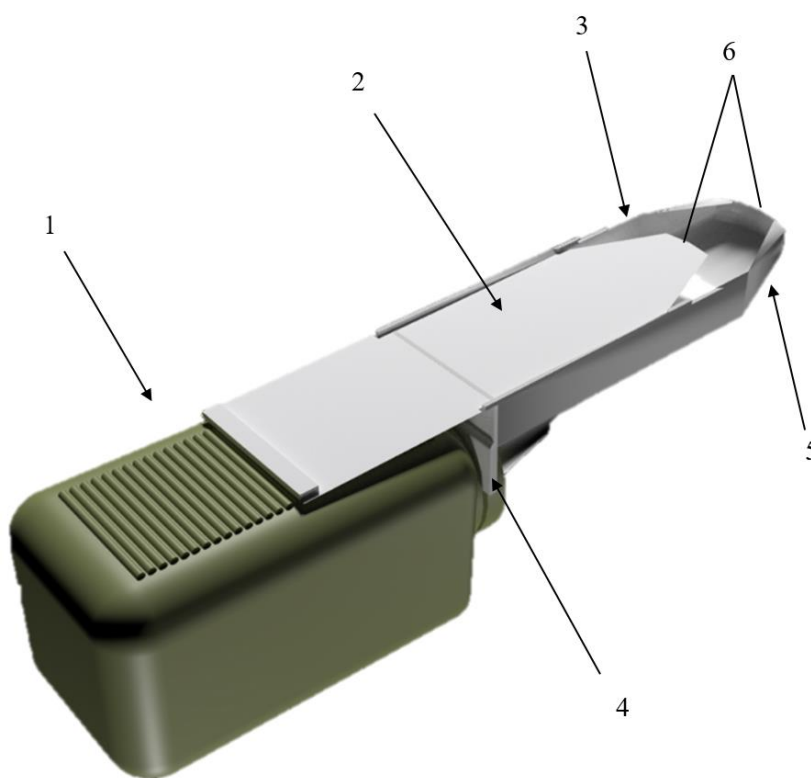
Трёхмерное изображение устройства. 1 – резервуар для пищи, 2 – скользящий ограничитель, 3 – корпус устройства, 4 – переходная муфта, 5 – рабочая часть, 6 – щель рабочей части.
